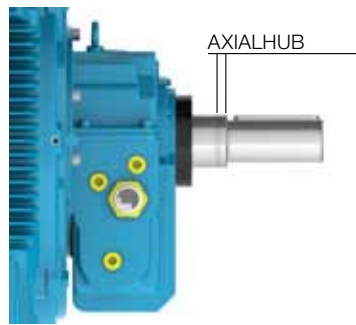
Axialhub eines mit Gleitlagern ausgestatteten Motors
